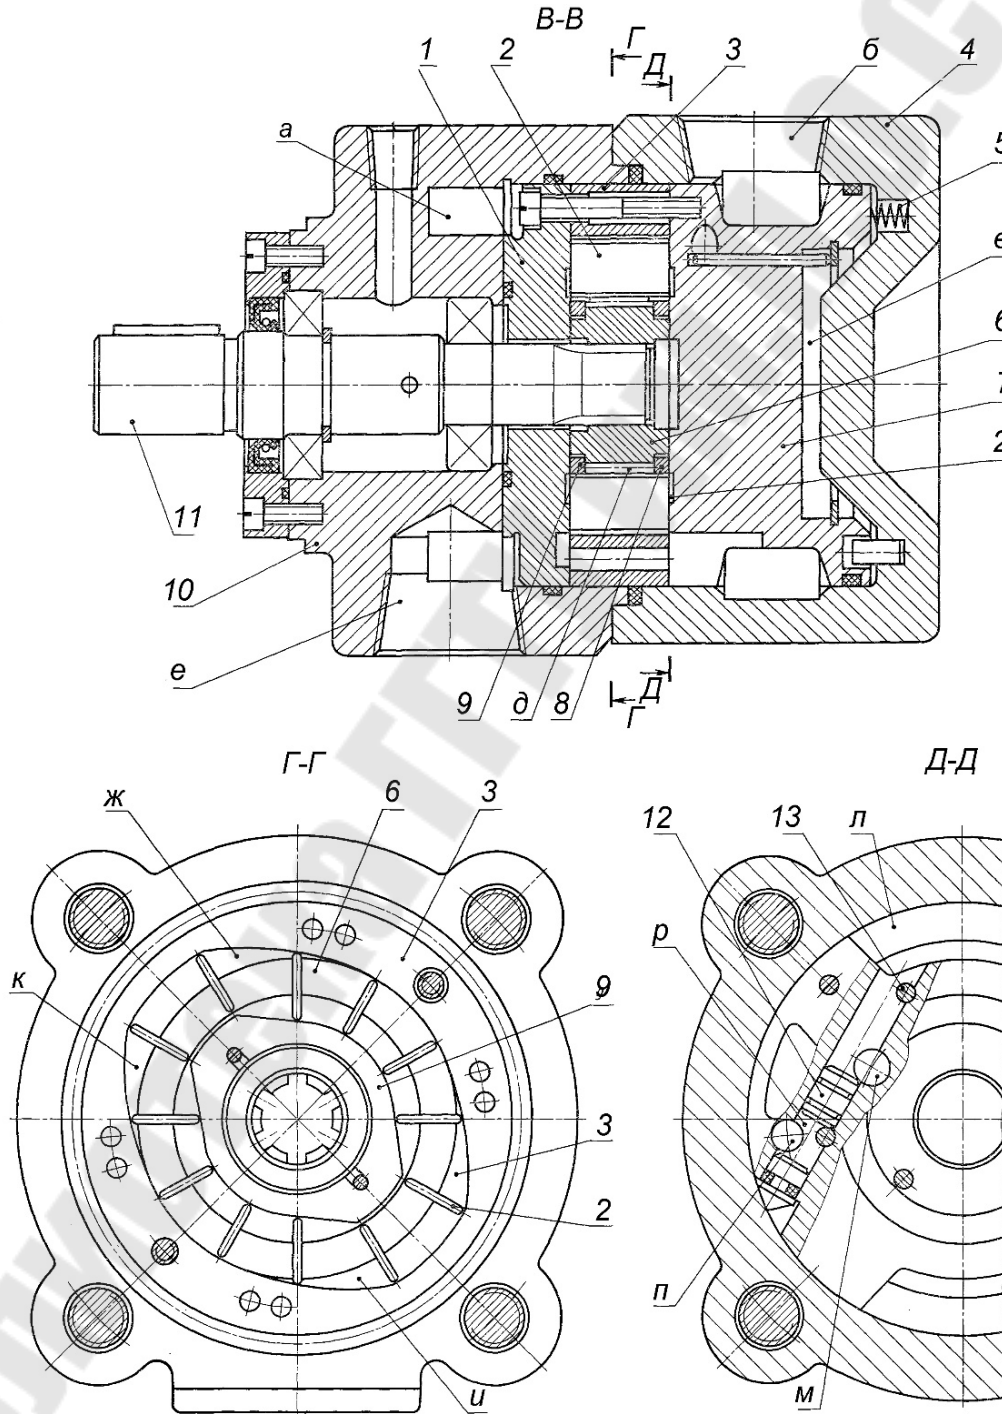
Пластинчатый гидромотор двойного действия типа Г16
